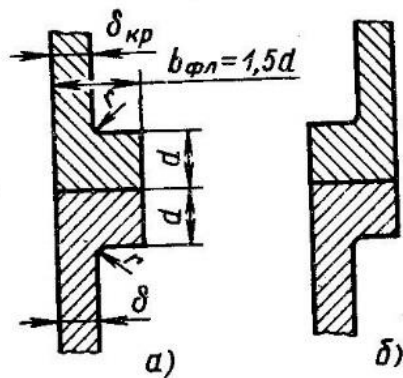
Безболтовое соединение крышки с корпусом:
